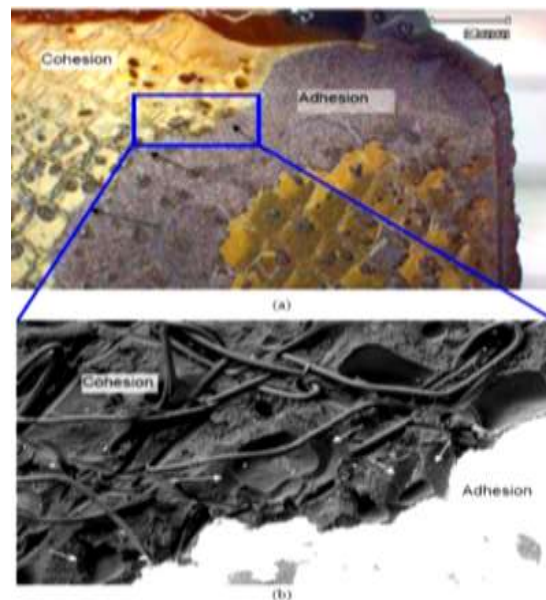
Observation d'une rupture mixte d'un joint collé par MEB [39]
